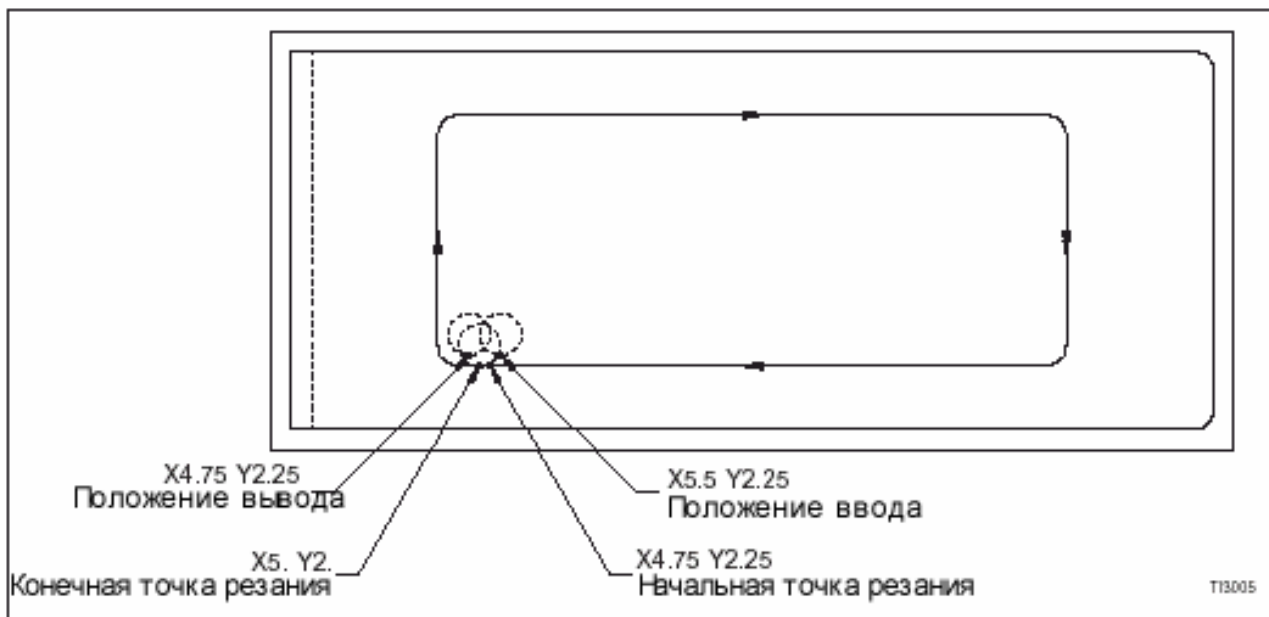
= Типовая (стандартная) заготовка: Траектория перемещения инструмента (контур глубокой выемки).
